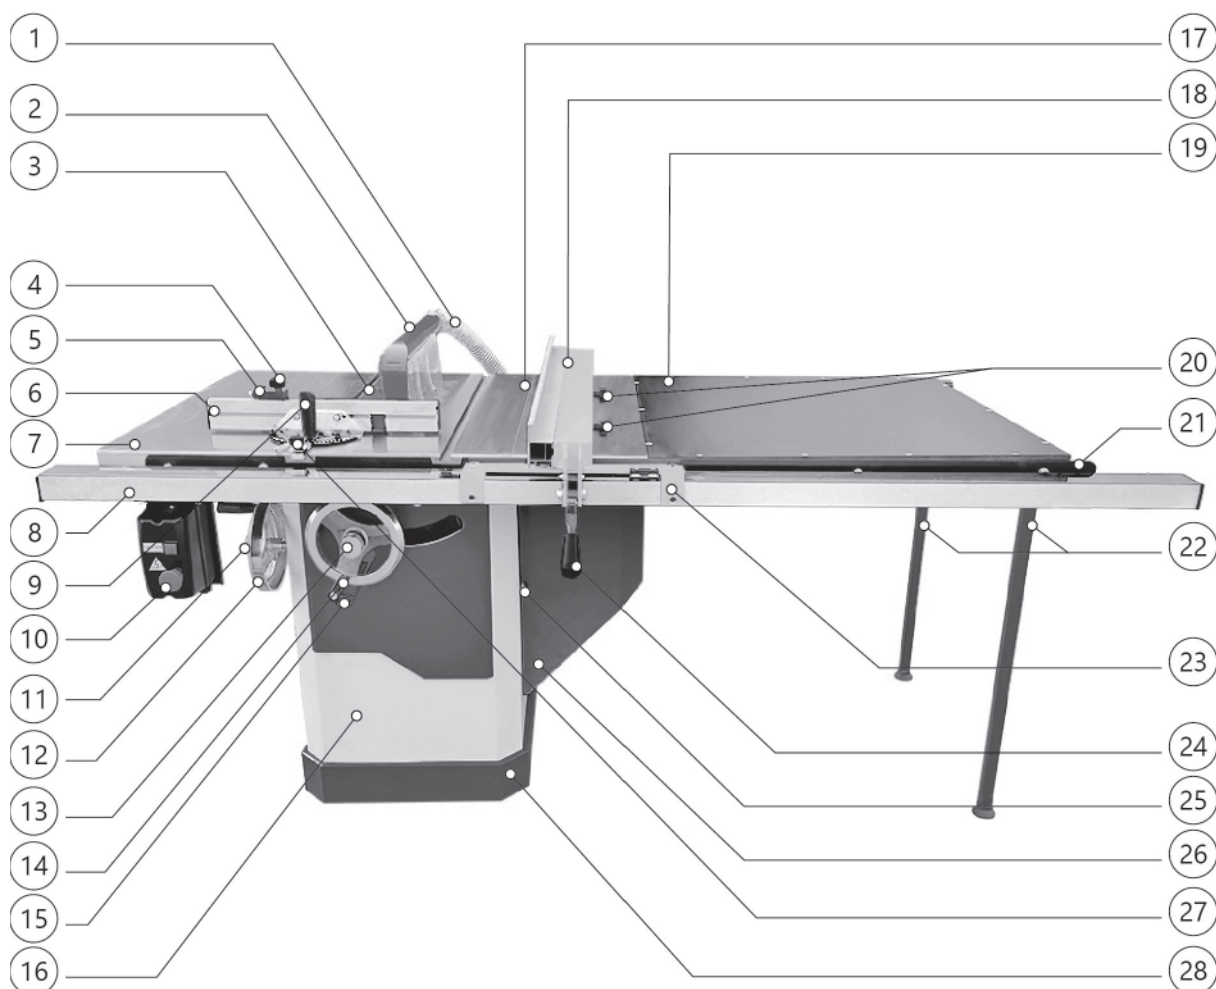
Основные элементы станка BELMASH LTS-250PE/400.
